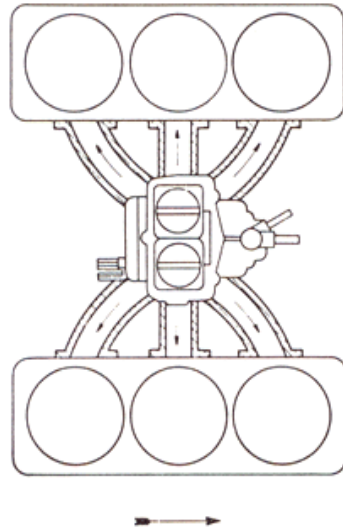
Diseño de colectores para motor de seis cilindros en V. Cada cuerpo del carburador alimenta tres cilindros.
